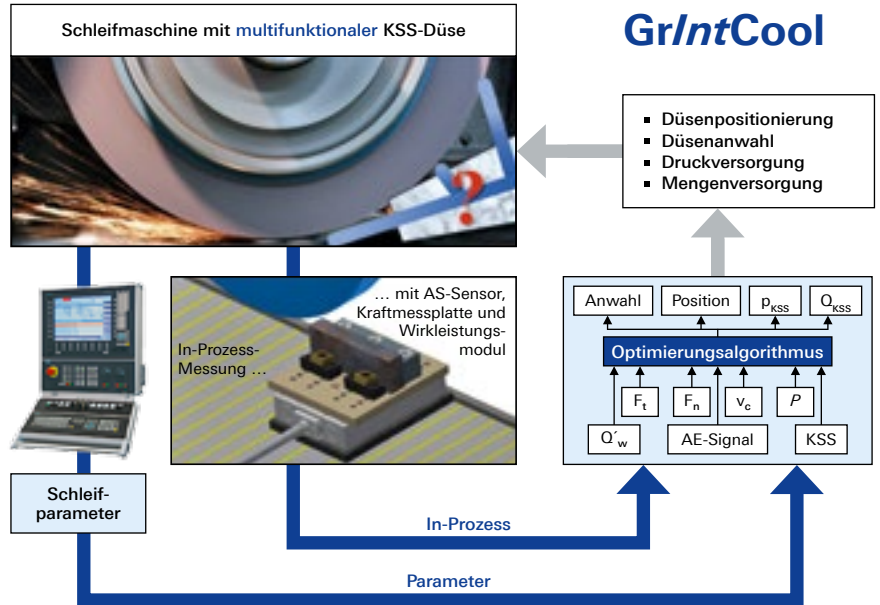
Übersicht des Projektes „GrIntCool – Grinding with intelligent coolant supply“
